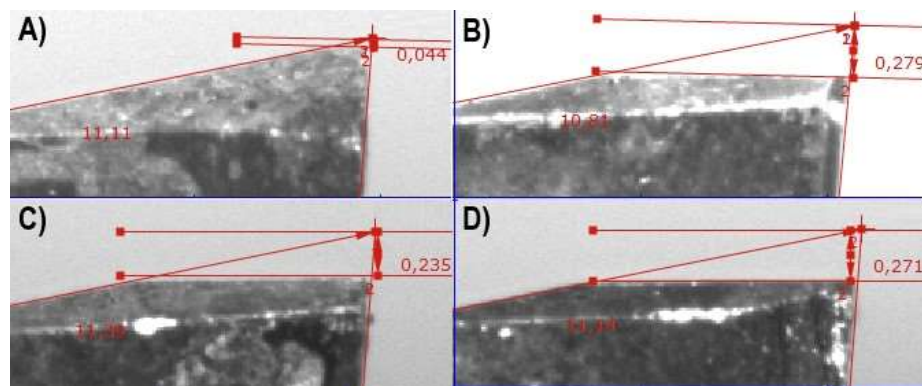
Medición de desgaste (VB) insertos grupo N4 NbC-VC 4hr Rev 540°X 1hora – maquinado acero 4140 a) 0,044mm b) 0,279mm c) 0,235mm d) 0,271mm.
